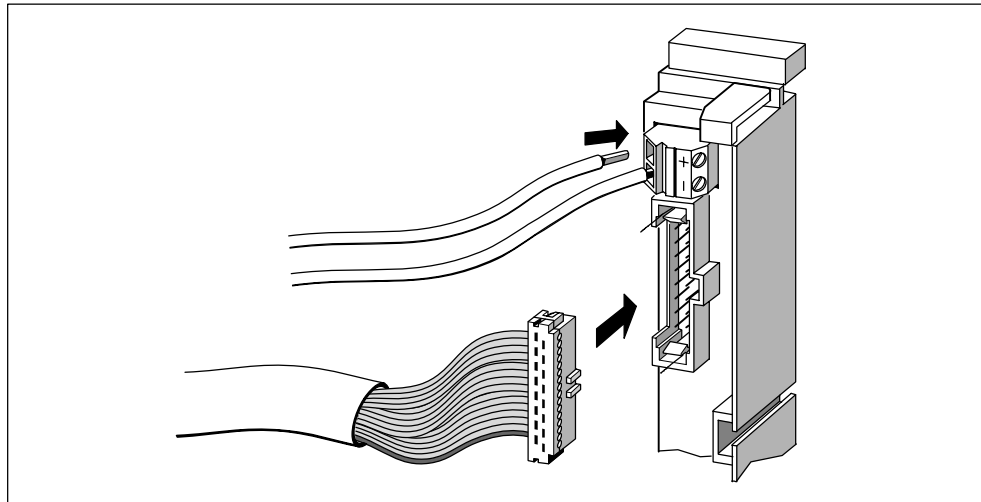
Verbindungsleitung in Frontsteckmodul einstecken
